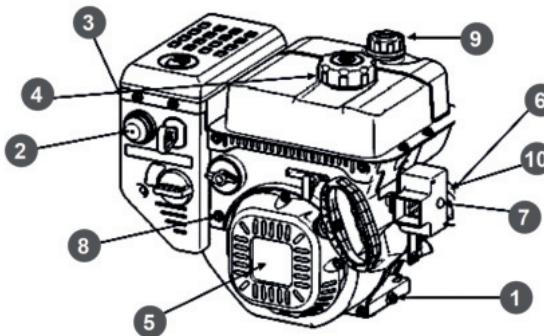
(Б) Основные узлы и органы управления двигателем SBG 560 E / SBG 620 E
